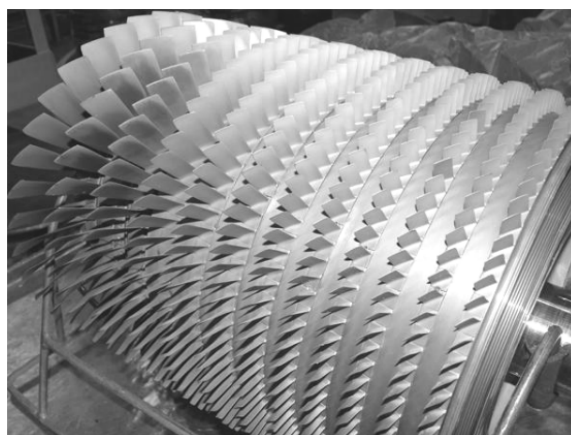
Загальний вигляд компресора авіаційного двигуна ТВ3-117 [5]
